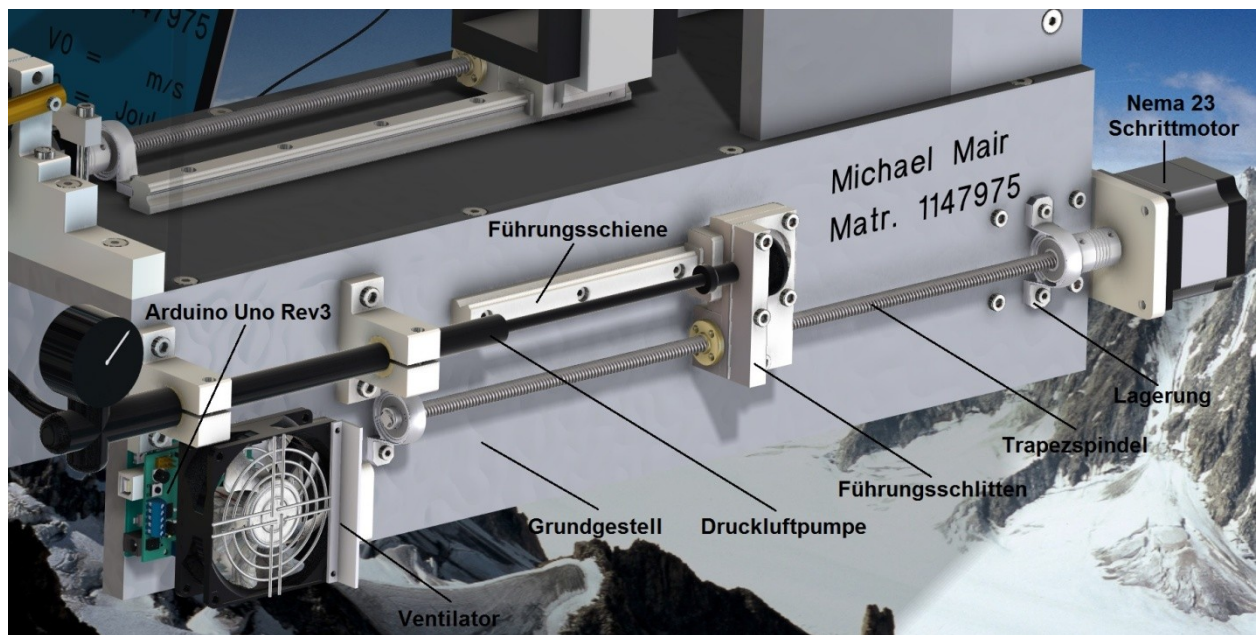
Detailansicht der 3D-Konstruktion (Startposition des Pumpvorgangs)
